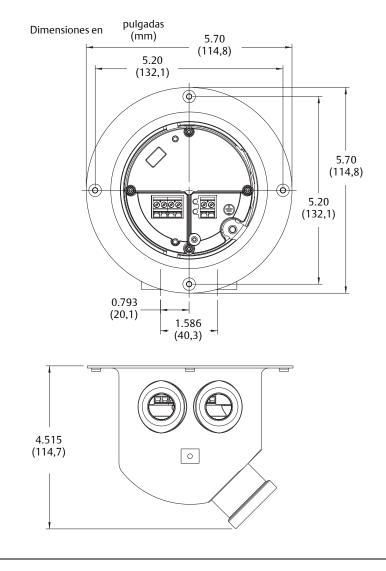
Dimensiones de la carcasa del transmisor para carcasa de acero inoxidable
